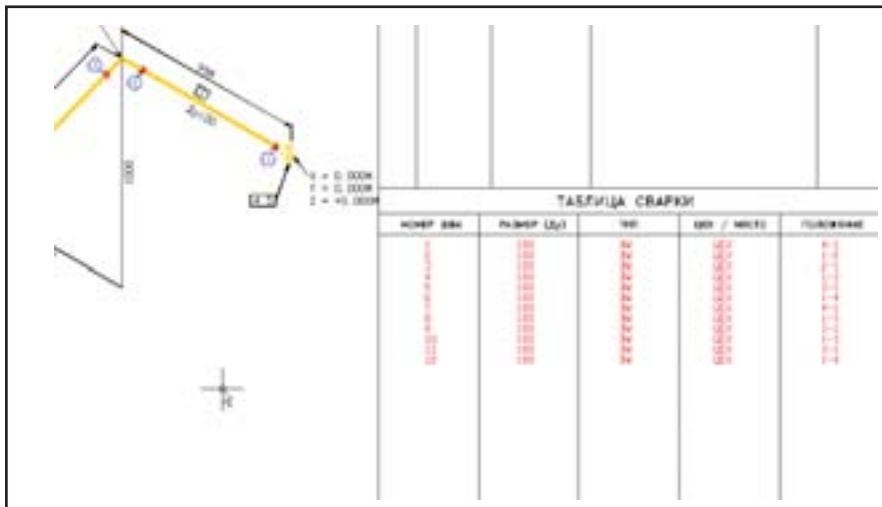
Нумерация сварных соединений позволяет ускорить работы, повысить их качество и упростить контроль
